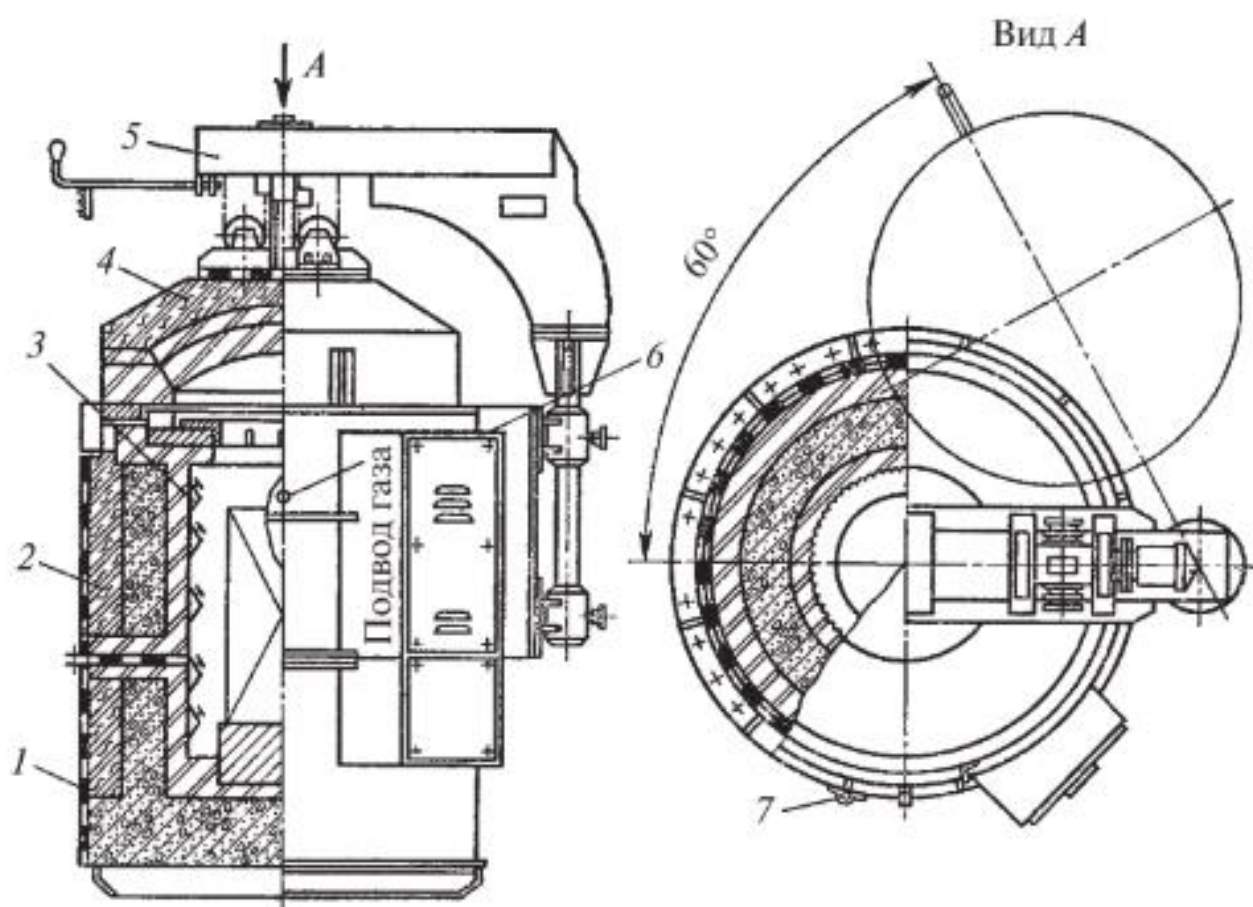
Конструкция шахтной печи: 1 – стальной кожух, 2 – футеровка, 3 – проволочные нагревательные элементы, 4 – крышка, 5 – механизм подъема крышки, 6 – подвод электроэнергии к нагревательным элементам, 7 – трубка для отвода газа
